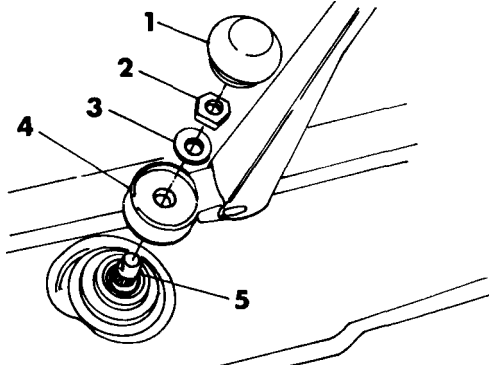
Крепление рычага стеклоочистителя. 1 - Крышка. 2 - Гайка. 3 - Шайба. 4 - Рычаг щетки стеклоочистителя. 5 - Ось.
